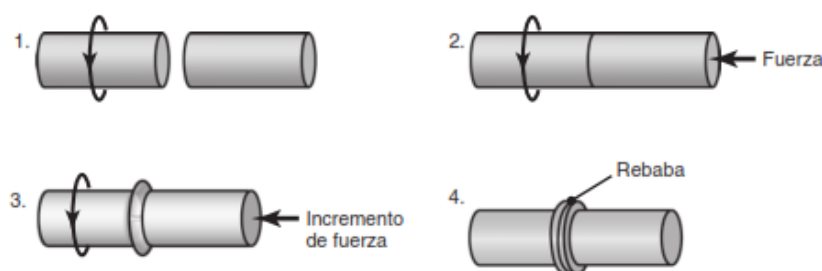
Secuencia de operaciones en el proceso de soldadura por fricción
